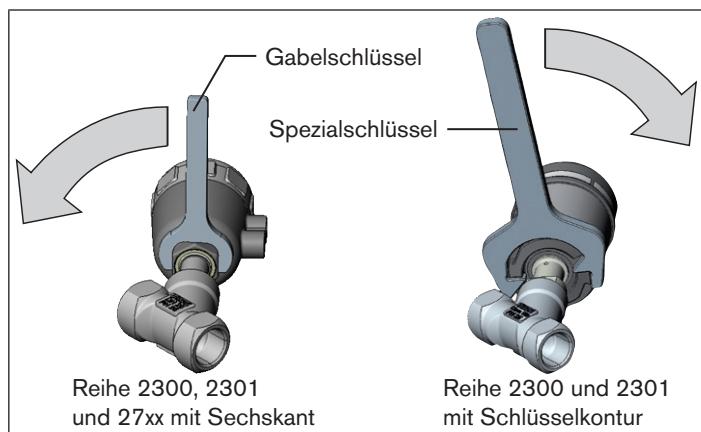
Drehen mit Spezialschlüssel / Gabelschlüssel
